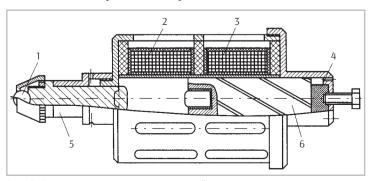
Схема инструмента ударного действия с электромагнитным приводом: 1 — индентор; 2 — катушка прямого хода; 3 — катушка обратного хода; 4 — амортизатор; 5 — фланец; 6 — боек
